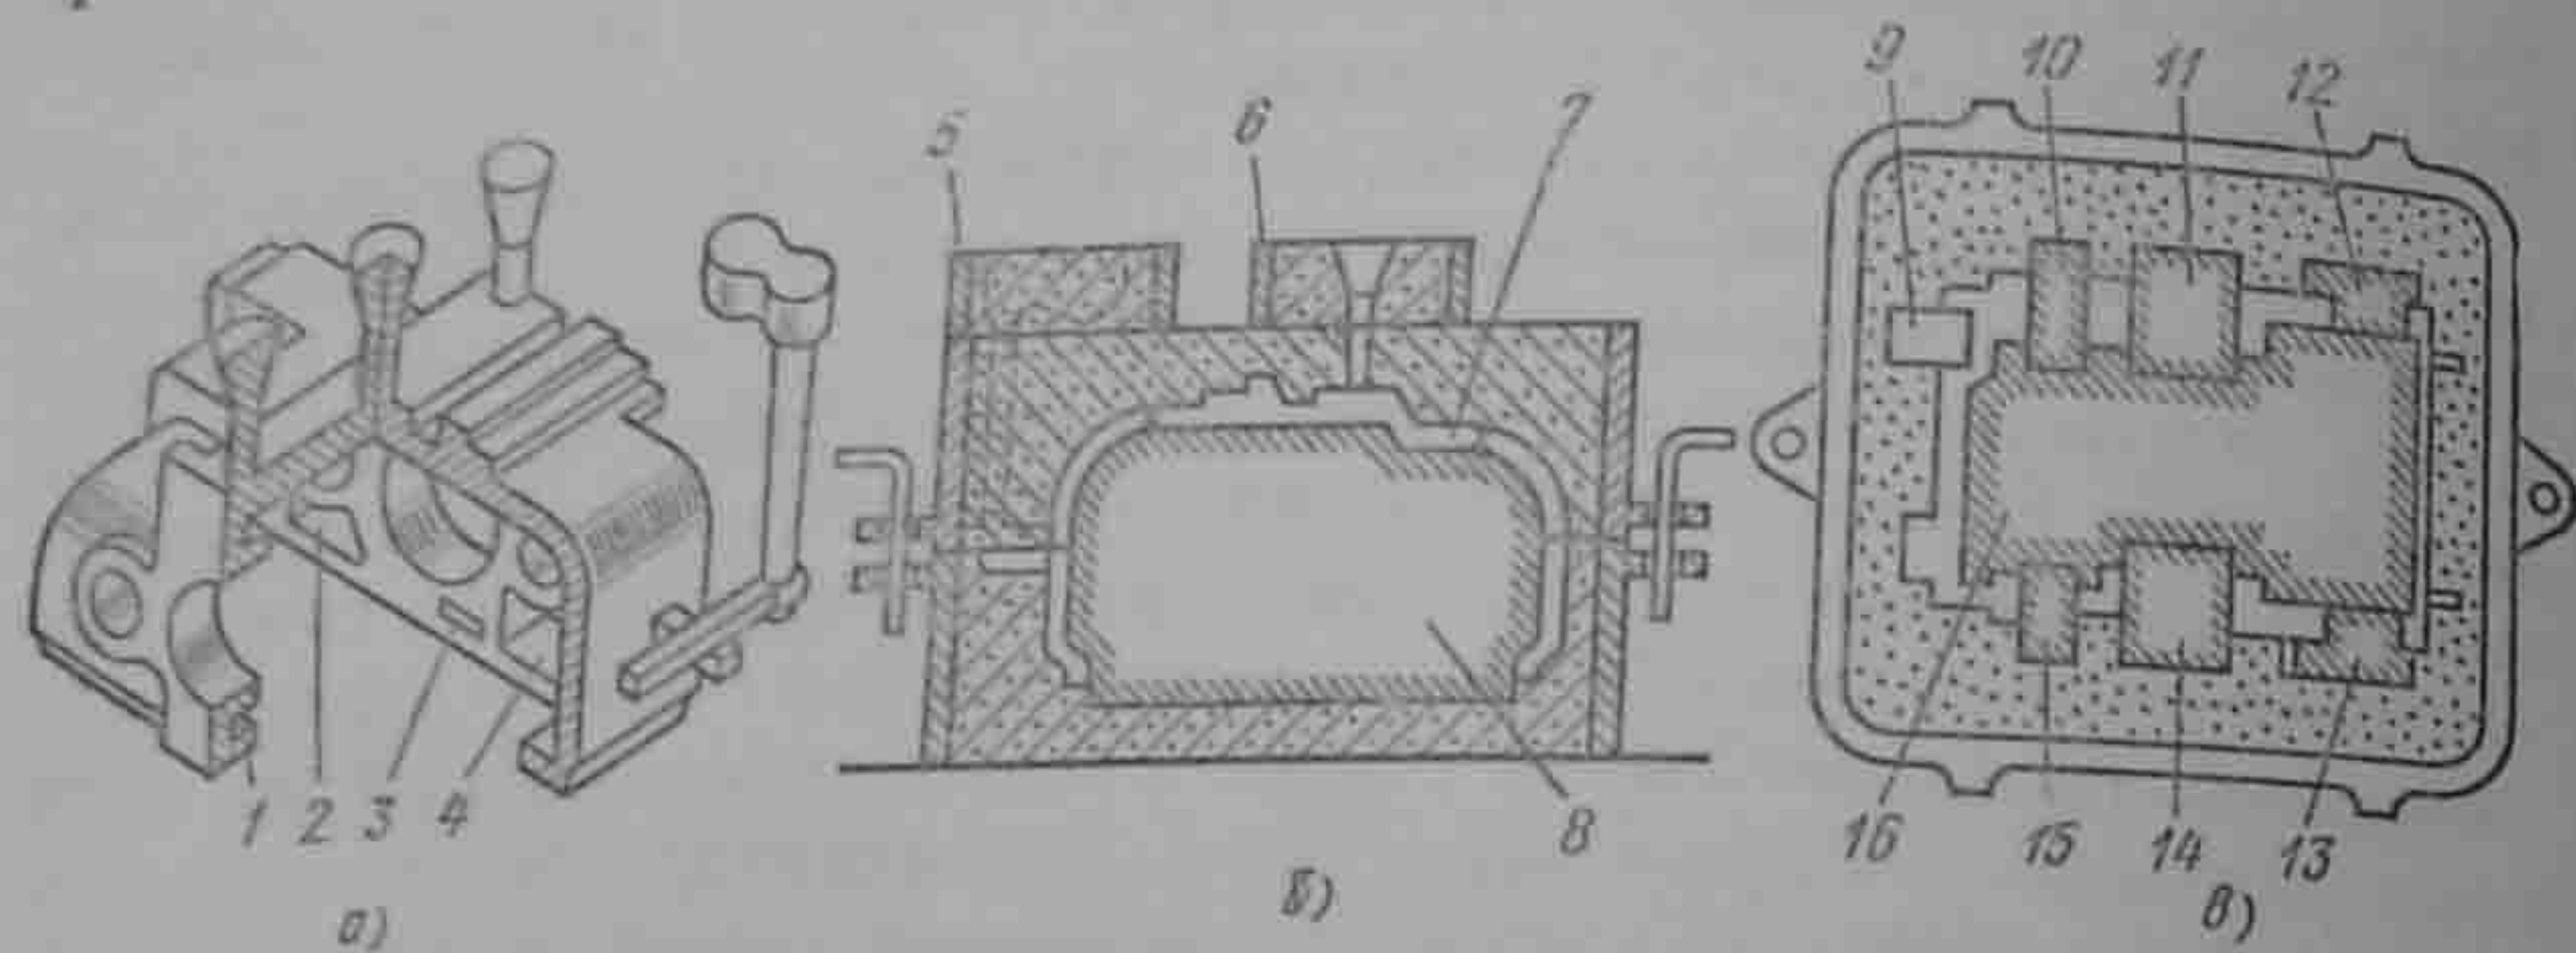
Сборка форм для отливки коробки скоростей револьверного станка: а — отливка; б, в — форма
